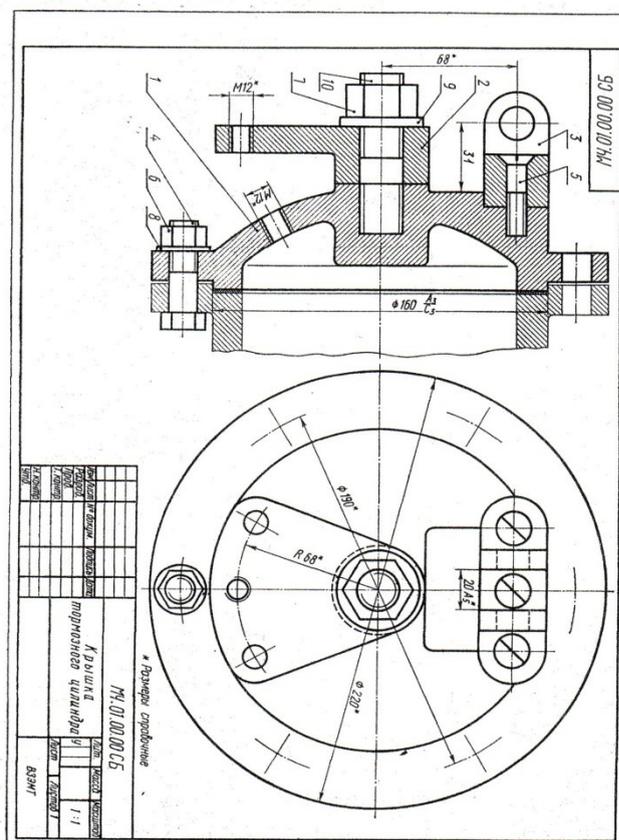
Сборочный чертёж «Крышка тормозного цилиндра»
